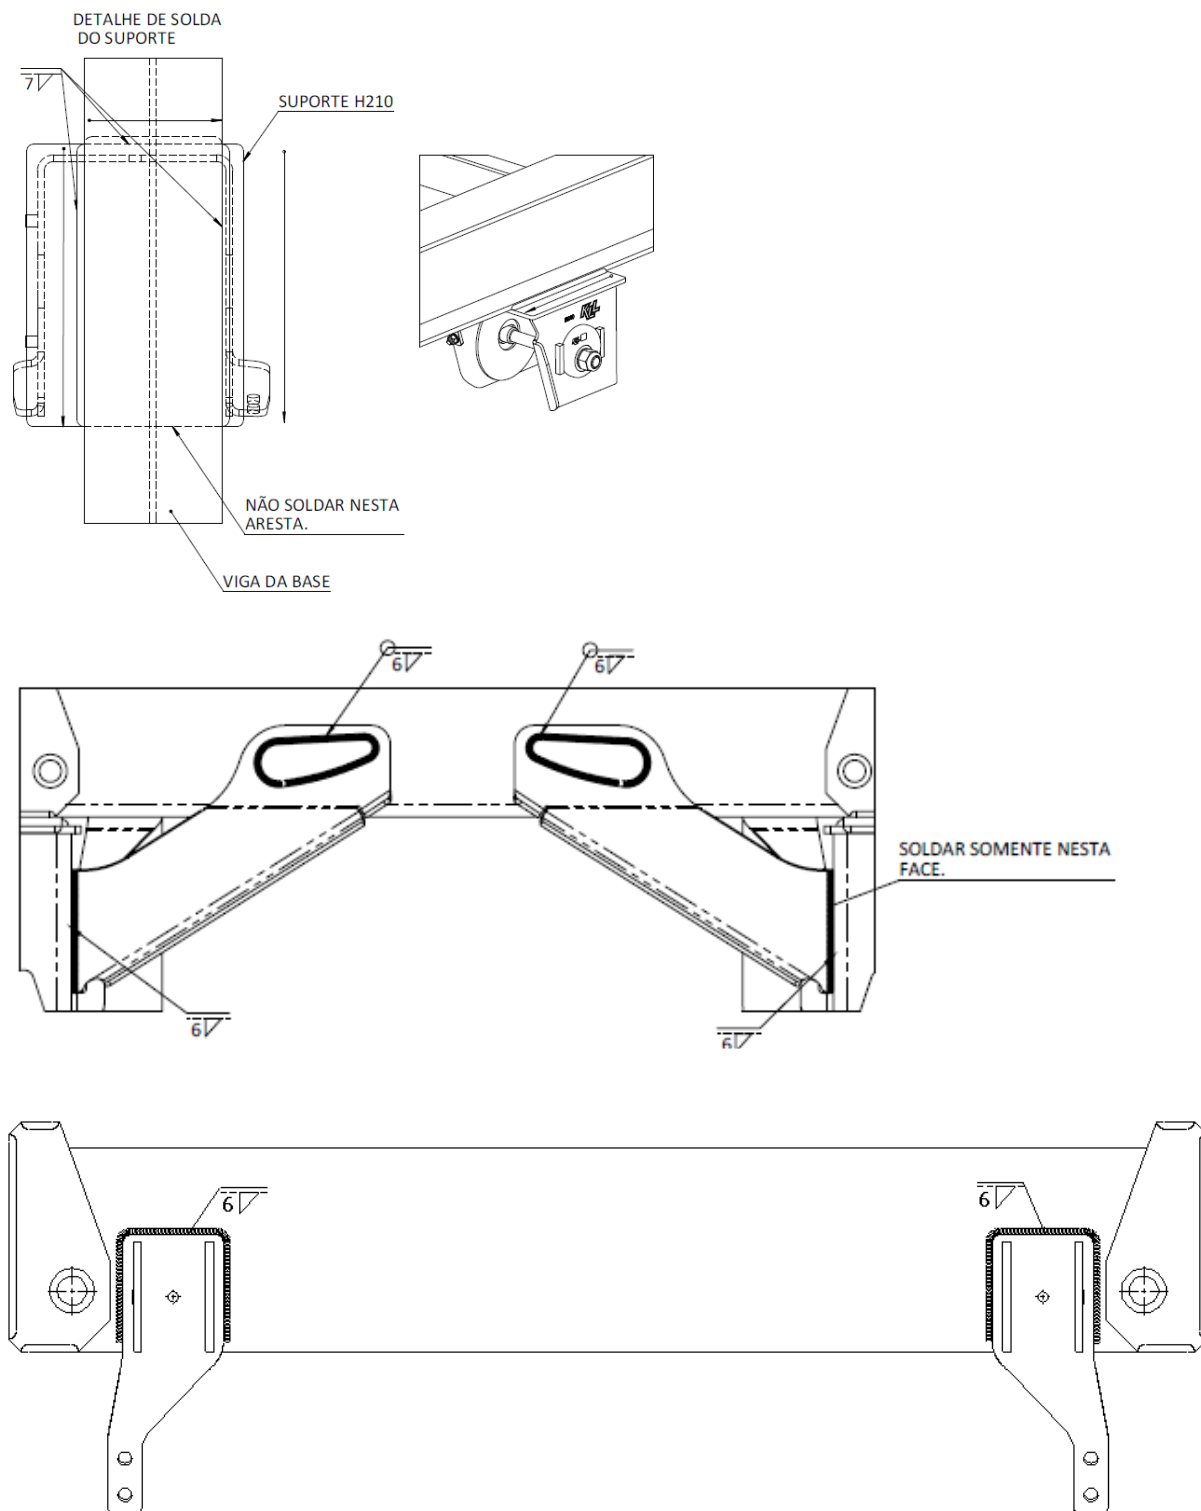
Solda do suporte frontal e reforço de ligação AIRSUPER H210
